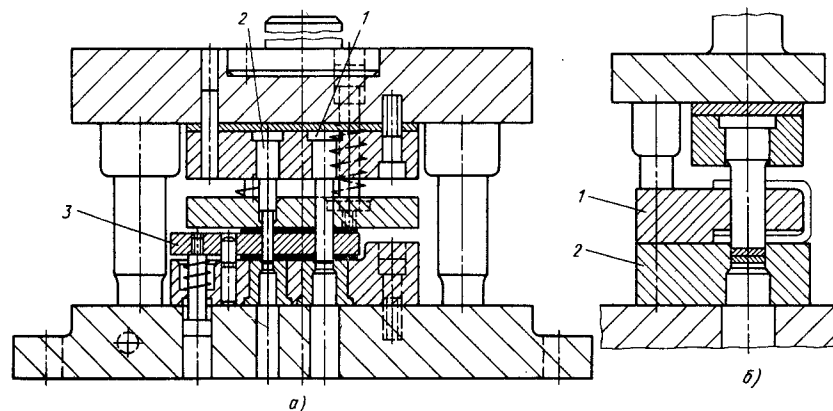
Сквозная пробивка отверстий одновременно в двух полках детали
